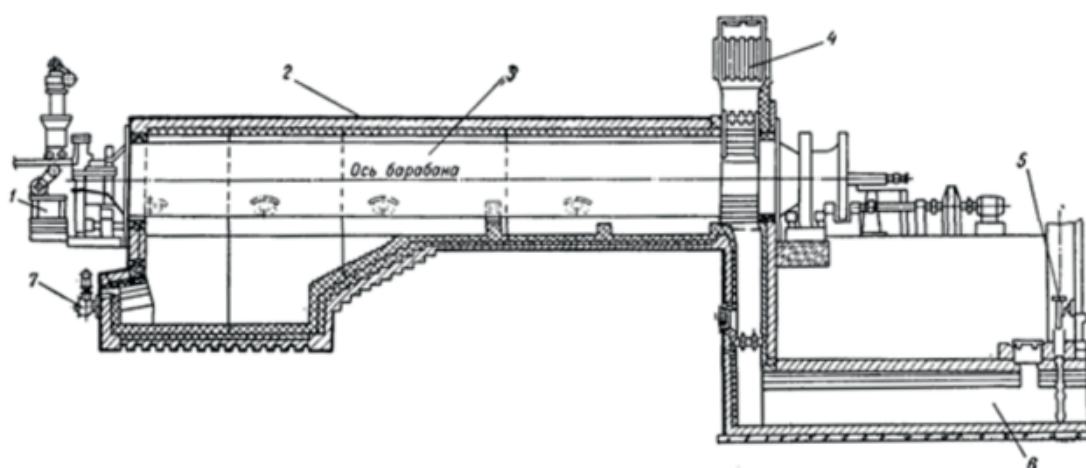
Продольный разрез содовой печи: 1 — механизм загрузки, 2 — футеровка, 3 — барабан, 4 — рекуператор, 5 — шлифер, 6 — боров, 7 — горелка
